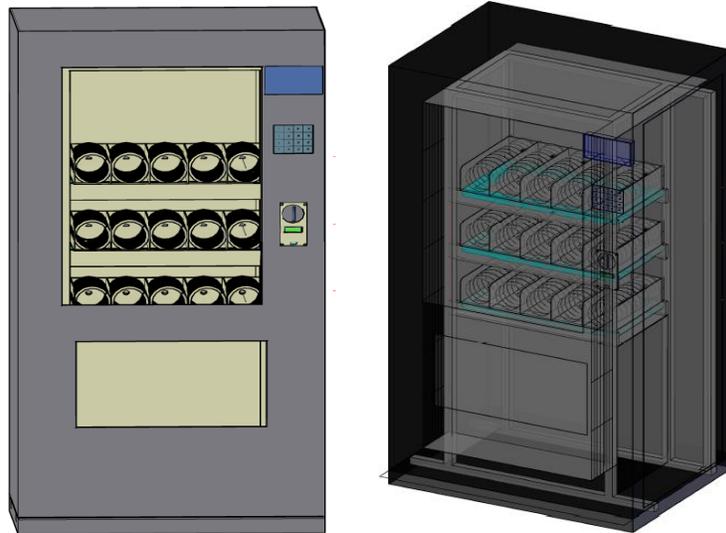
Diseño 3D, parte frontal e interna de la máquina expendedora. Fuente propia.
